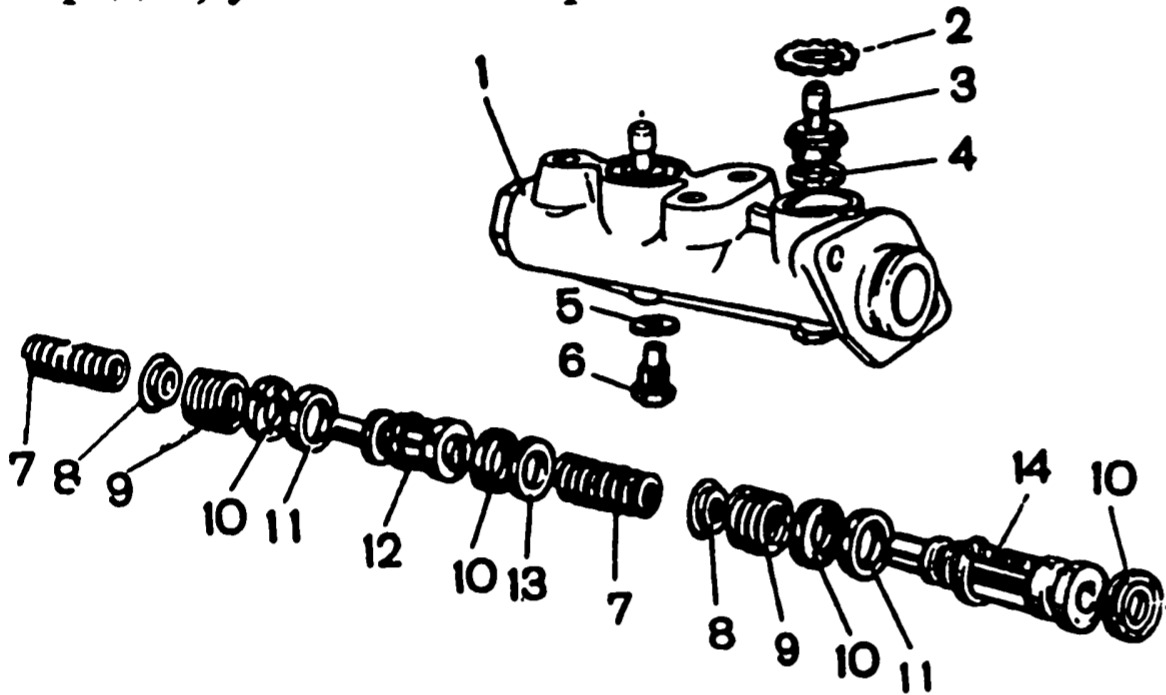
Детали главного цилиндра привода тормозов: 1 - корпус цилиндра; 2 - стопорная шайба; 3 - штуцер; 4 - уплотнительная прокладка; 5 - уплотнительная шайба; 6 - стопорный винт поршня; 7 - возвратные пружины поршней; 8 - чашка; 9 - прижимная пружина уплотнительного кольца; 10 - уплотнительное кольцо; 11 - распорное кольцо; 12 - поршень привода задних тормозов; 13 - шайба; 14 - поршень привода передних тормозов
